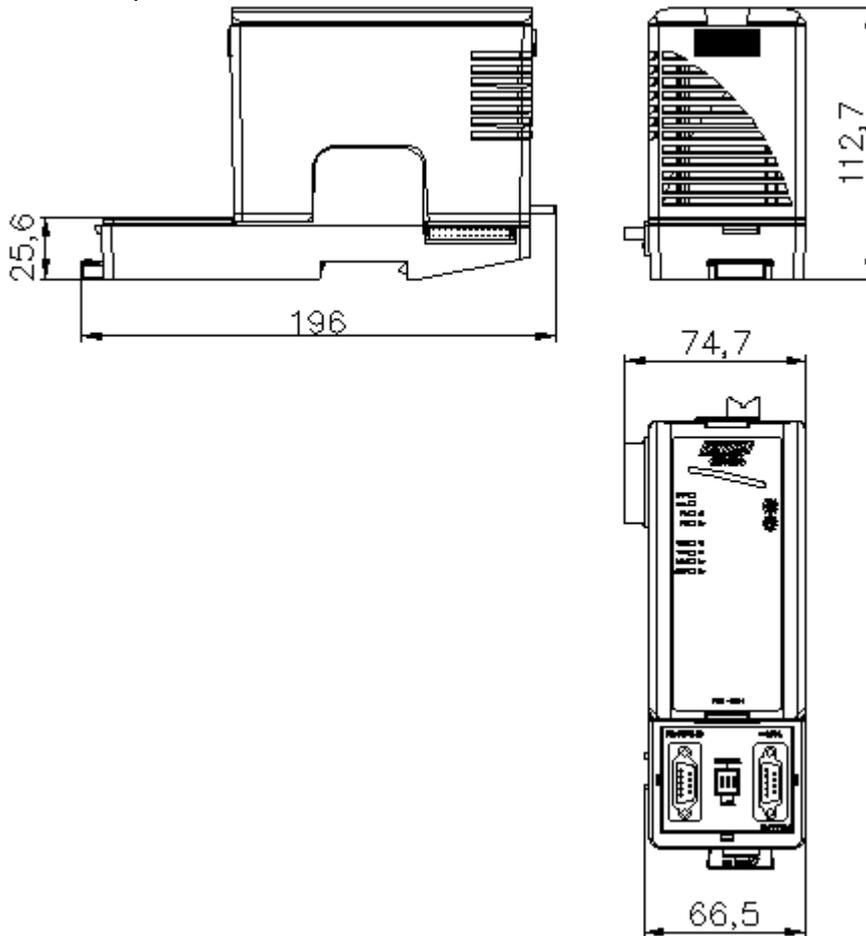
Dimensional mecânico do módulo MFI-PBM
